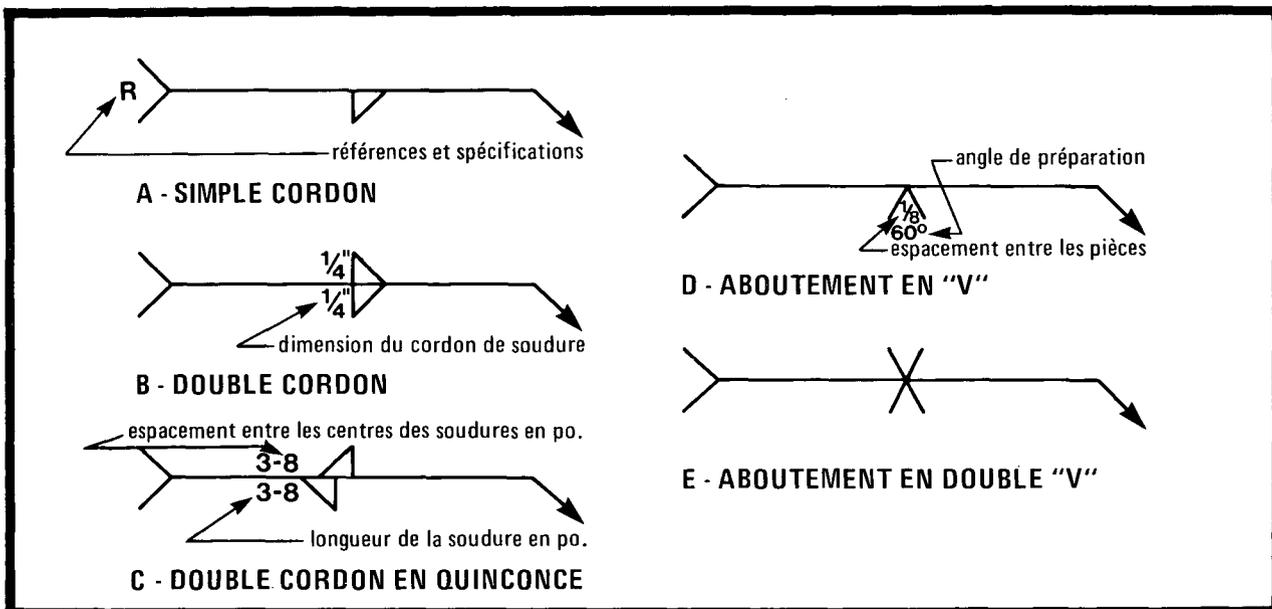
SYMBOLES DE SOUDAGE
